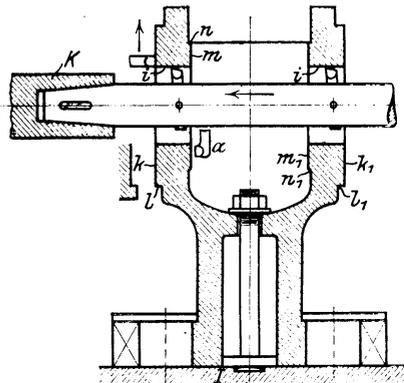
Bearbeitung des Loches für den Kreuzkopfbolzen.
